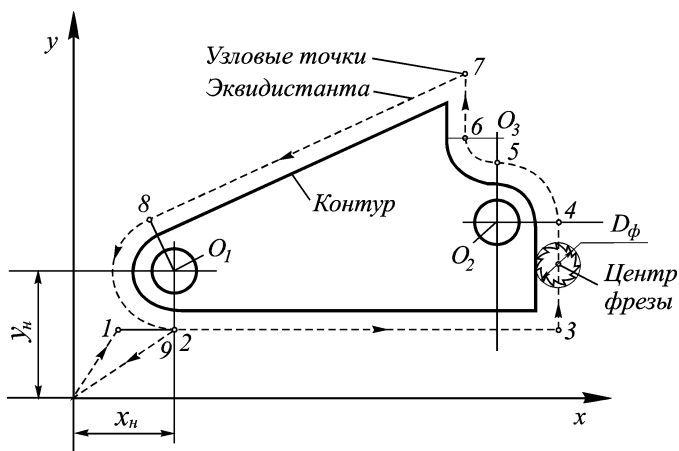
Схема контурного непрерывного управления при фрезеровании
